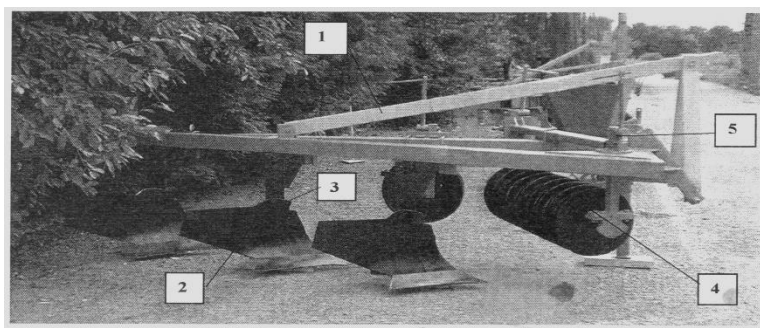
Конструктивна схема і загальний вид полицевого плуга, оснащеного дисковою батареєю.
